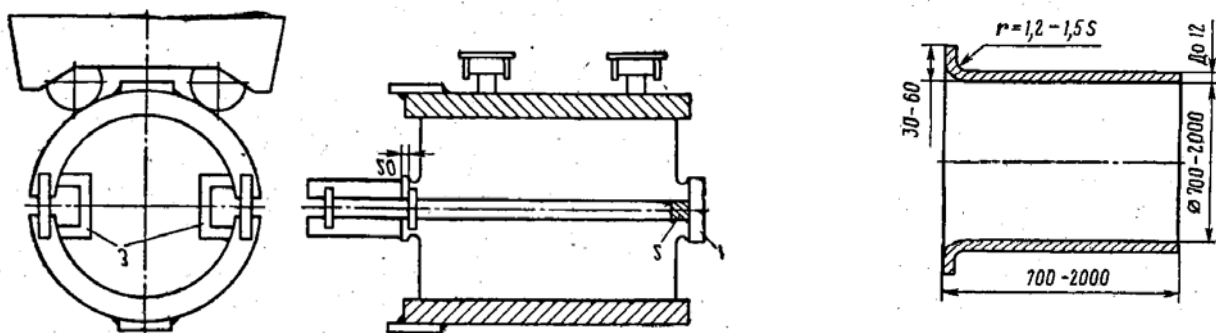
Сборка обечайки под электрошлаковую сварку
